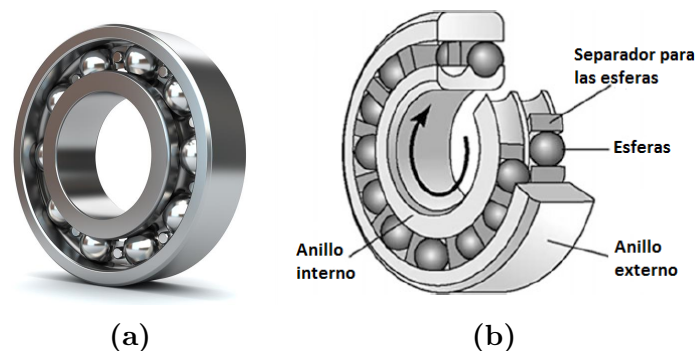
a) Rodamiento típico [51]. b) Partes de un rodamiento [36].
